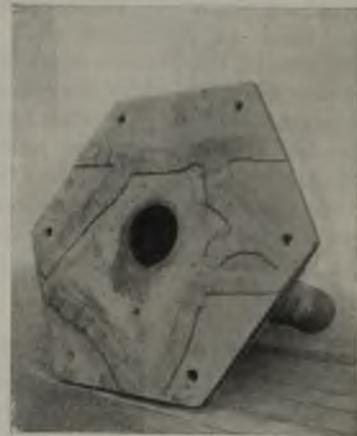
c. Ständerplatte nach der Schweißung.
